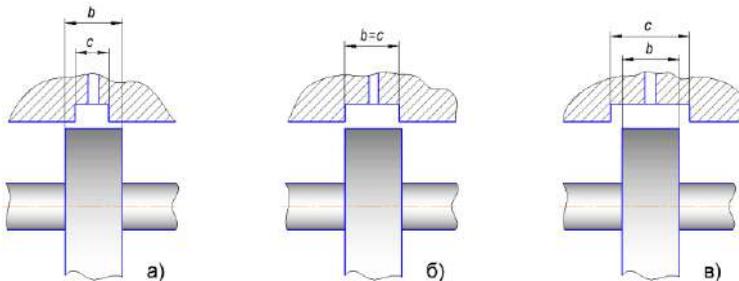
Схеми перекриттів робочих вікон в золотникових розподільниках: а – з нульовим перекриттям; б – з позитивним перекриттям; в – з негативним перекриттям
